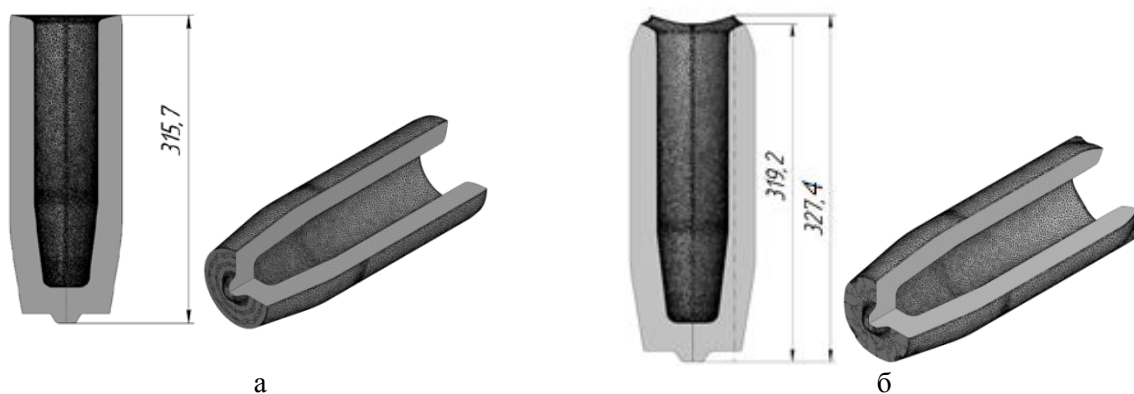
Кінцеві форми та розміри половин виробів та загальні вигляди з розрізом: а – після видавлювання заготовки круглого перерізу, б - після видавлювання заготовки квадратного перерізу
